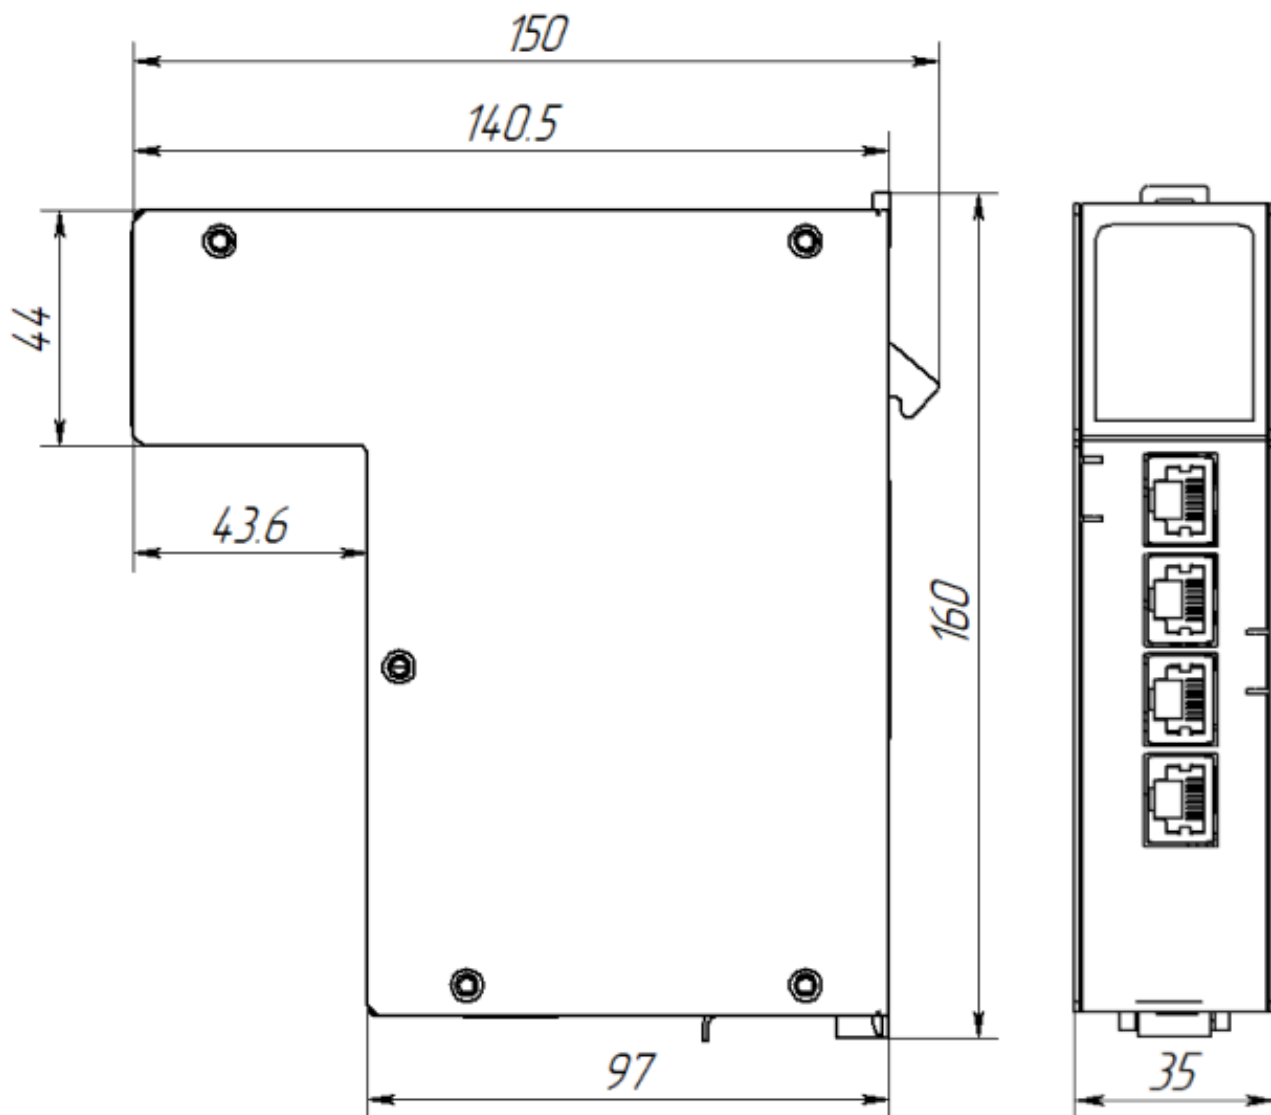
Габаритные и присоединительные размеры модуля CP-12 в металлическом корпусе
